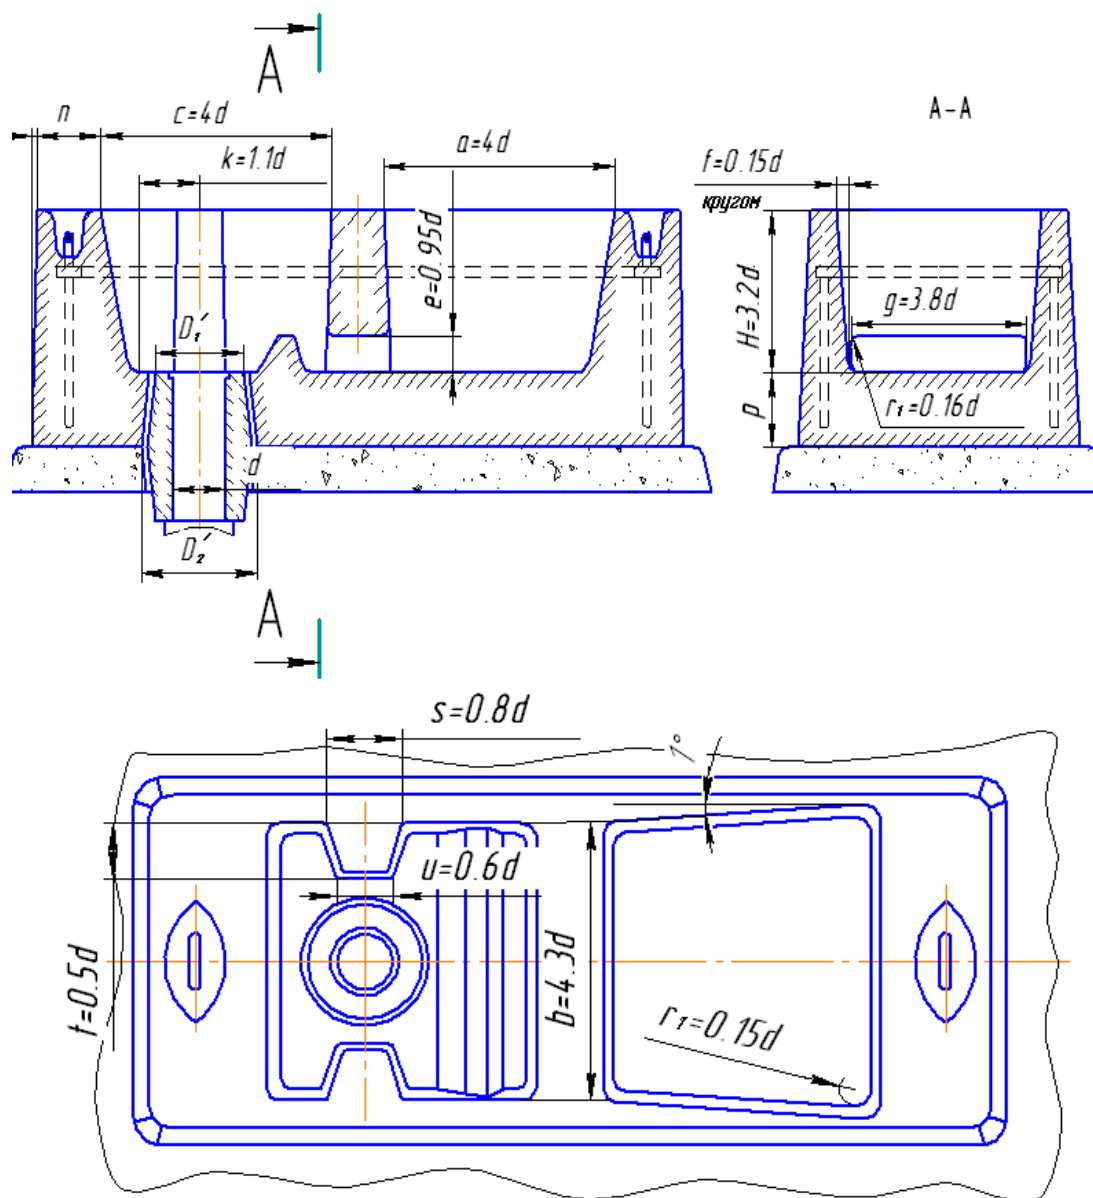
Эскиз литниковой чаши-нарощалки с перегородкой, обеспечивающей расход металла до 50 кг/с
